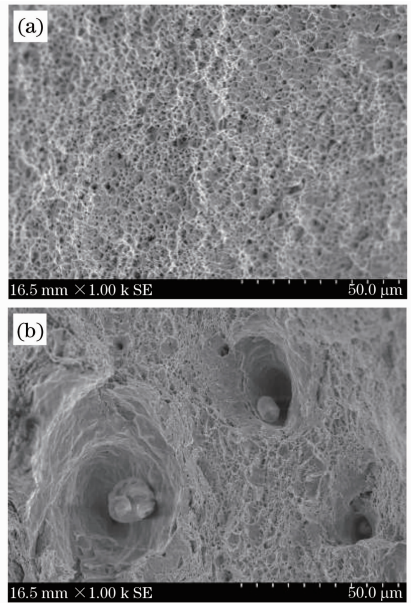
焊缝(a)和母材(b)的断口微观形貌
